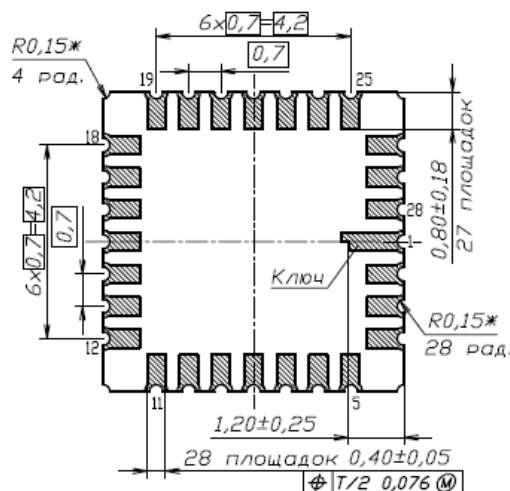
Габаритный чертеж корпуса МК 5123.28-1
